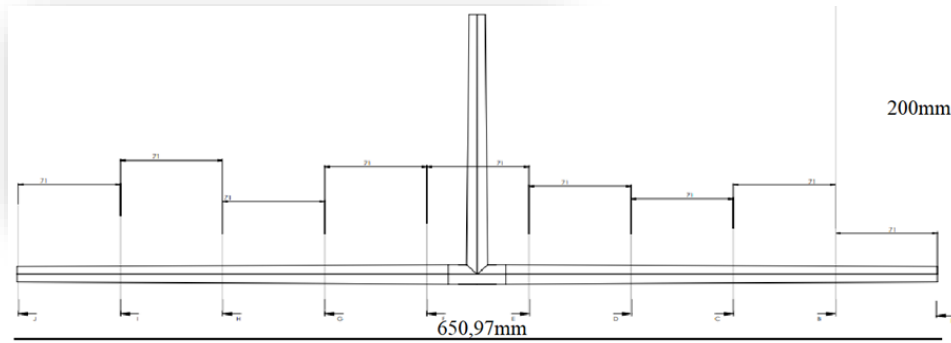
Plano Estabilizador Vertical Y Horizontal. [Autor]
